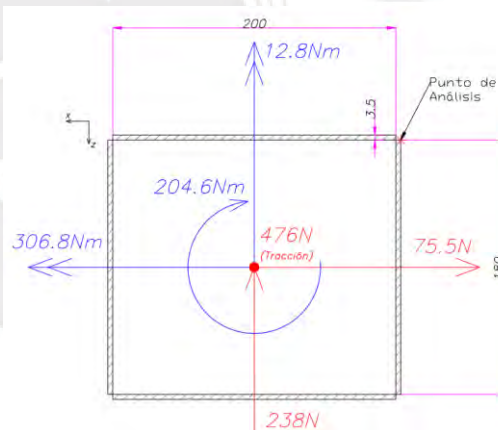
Cordón de soldadura Cabezal-Bancada
